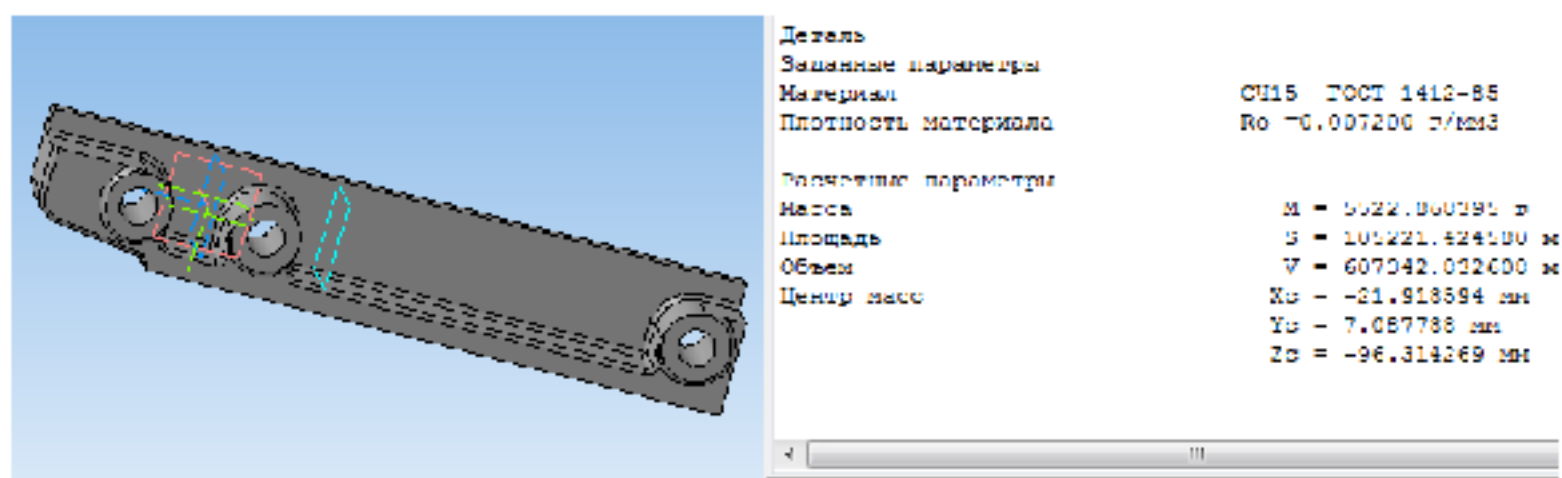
3D-модель заготовки (лиття в піщано-глинисті форми)
